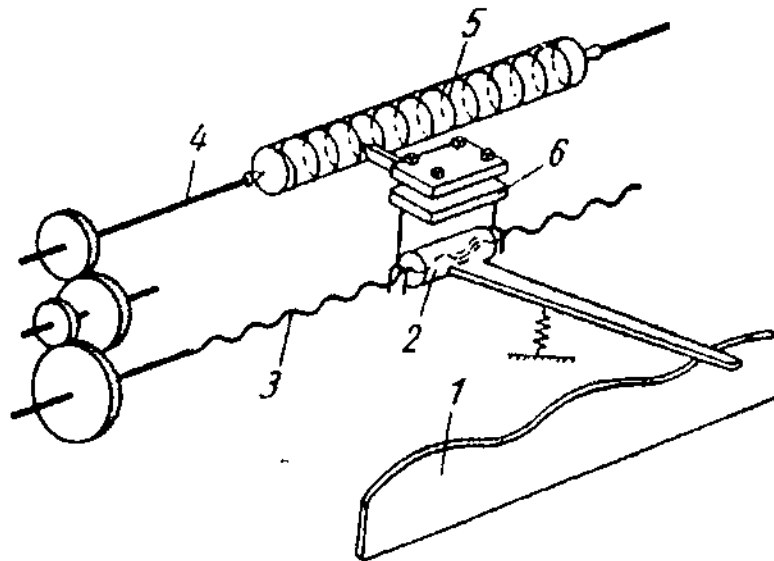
Схема нарезания резьбы на токарно-винторезном станке с применением коррекционной линейки.
